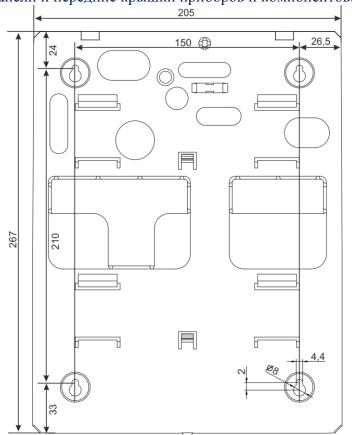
Установочный чертеж основания корпуса ППКО и БА-18
